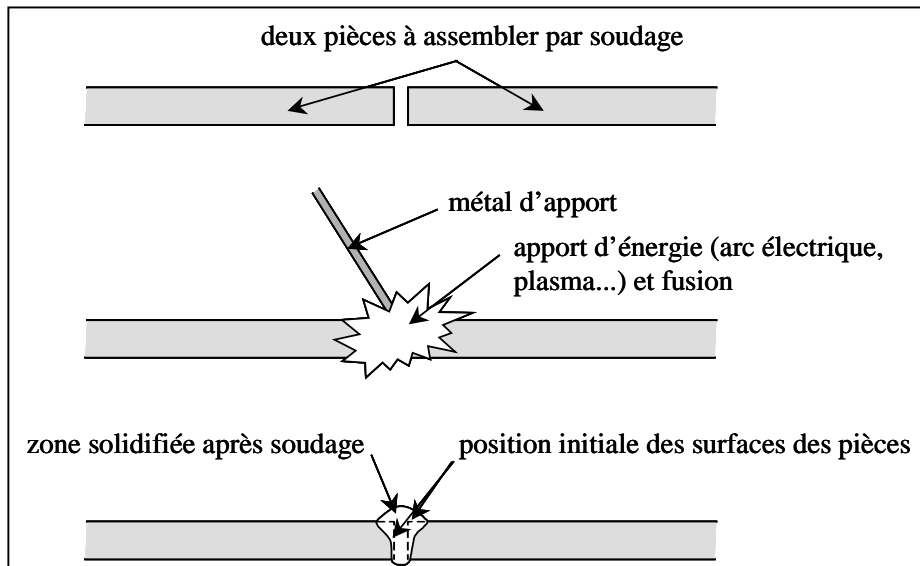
Principe du soudage. Noter la différence avec le brasage : la fusion locale des pièces à assembler.
